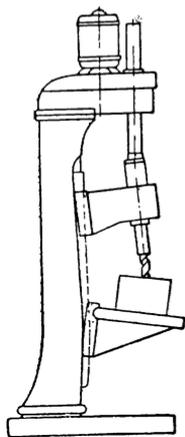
Деформация станка под действием сил резания. (утрированный вид)
